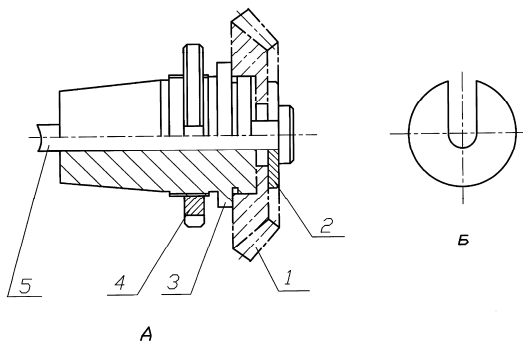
Приспособление для нарезания конического зубчатого колеса:
